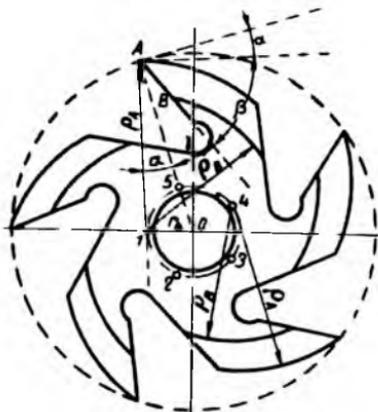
Способ построения затылка зуба фрезы по дуге окружности, центр которой смещен относительно центра фрезы
